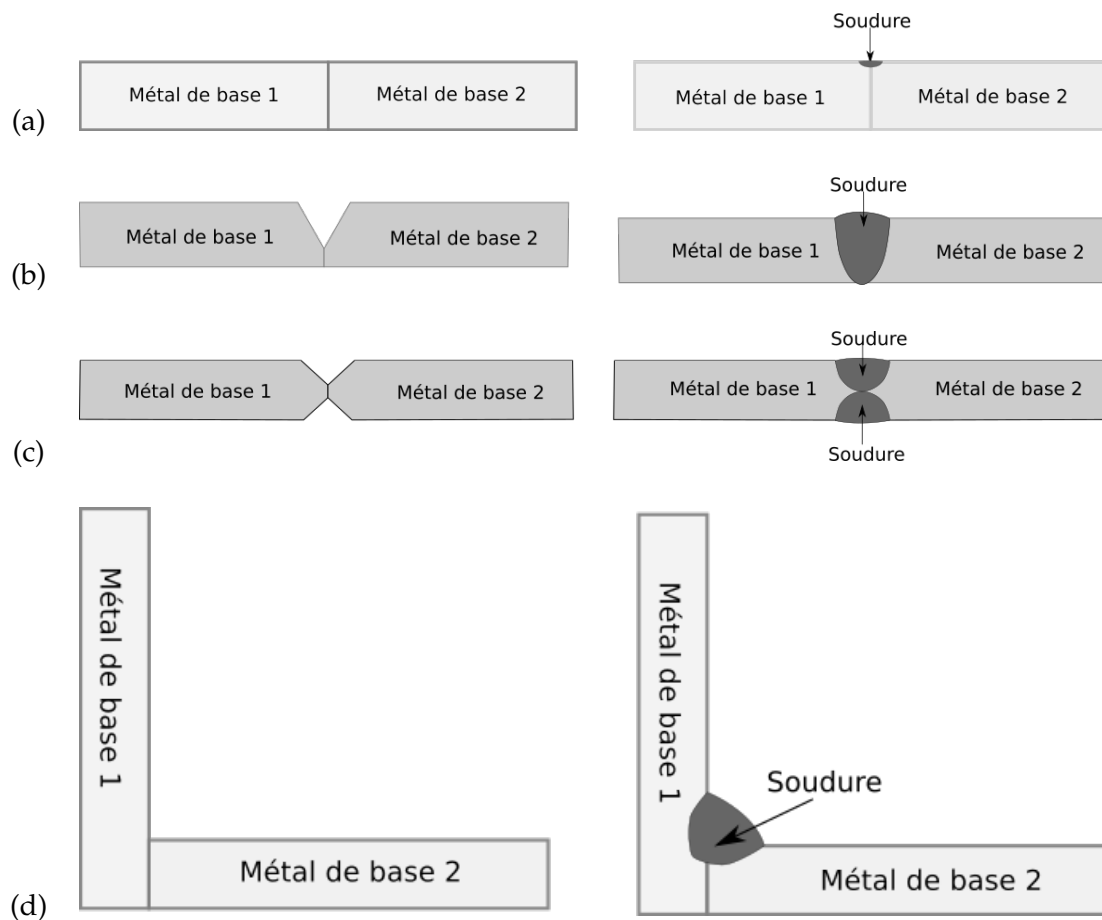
Exemples de types d'assemblages rencontrés lors d'une opération de soudage; (a) soudure bout à bout sans apport de métal; (b) soudure avec métal d'apport dans un chanfrein en V; (c) soudure avec métal d'apport dans un chanfrein en X; (d) soudure en angle avec apport de métal.
